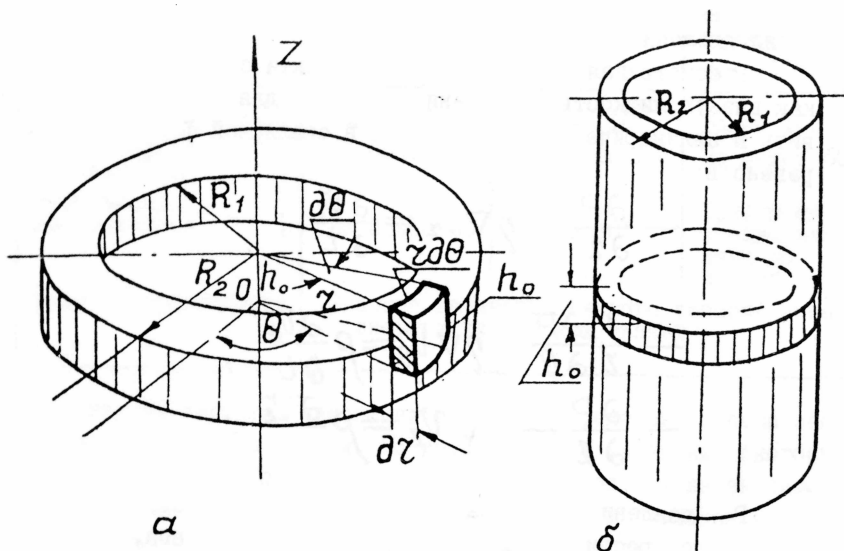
Расчетная схема течения расплава в процессе осадки при стыковой сварке: а - расчетный элемент; б - сваренные трубы
